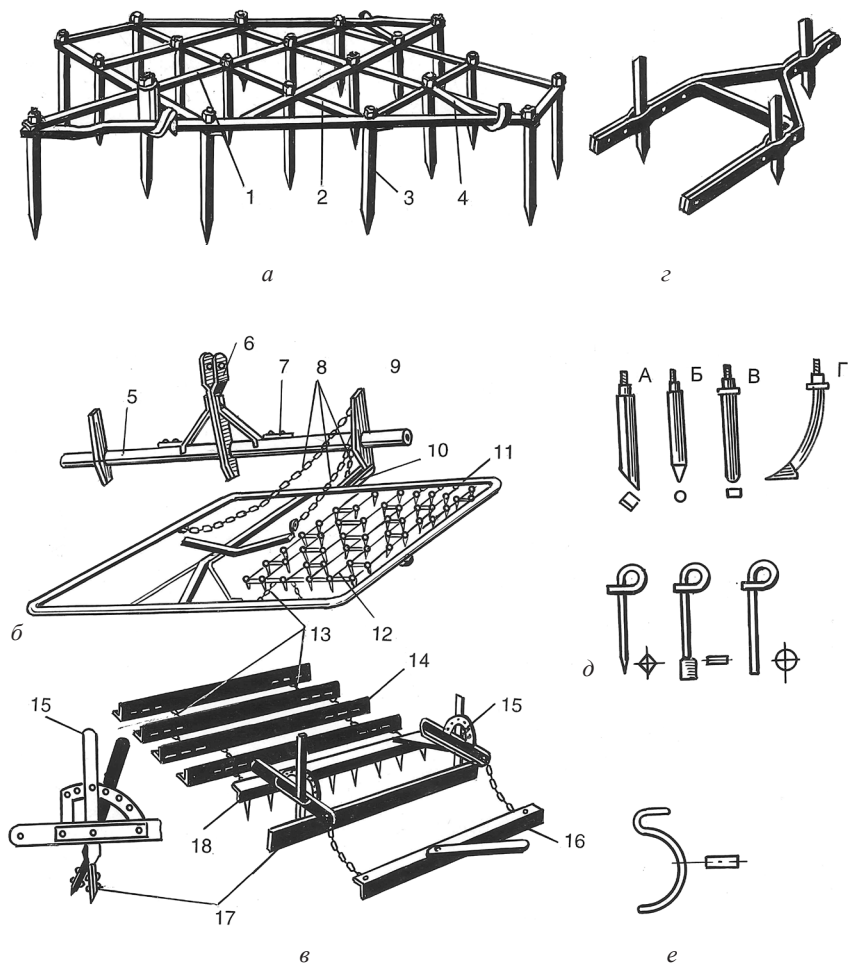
Зубовые бороны и их рабочие органы: *а* – зубовая тяжелая; *б* – сетчатая; *в* – шлейф-борона; *г* – звено луговой бороны с ножевыми зубьями; А – зуб квадратного сечения; Б – зуб круглого сечения; В – зуб овального сечения; Г – лапчатый зуб; *д* – зубья сетчатой бороны; *е* – зуб пружинной бороны; 1, 2 – планки рамы; 3 – зуб; 4 – прицепное устройство; 5 – брус навески; 6 – стойка; 7 – палец; 8, 13 – цепи; 9 – кронштейн; 10 – тяга; 11 – рамка; 12 – сетчатое полотно; 14 – шлейф; 15 – регулятор наклона ножа; 16 – вага; 17 – нож; 18 – уголок-гребенка
